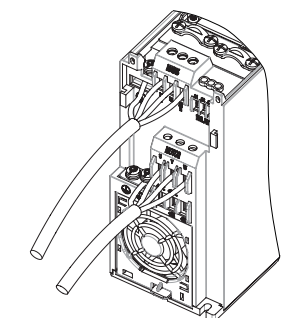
Montagem dos Cabos de Aterramento, Rede Elétrica e Motor
